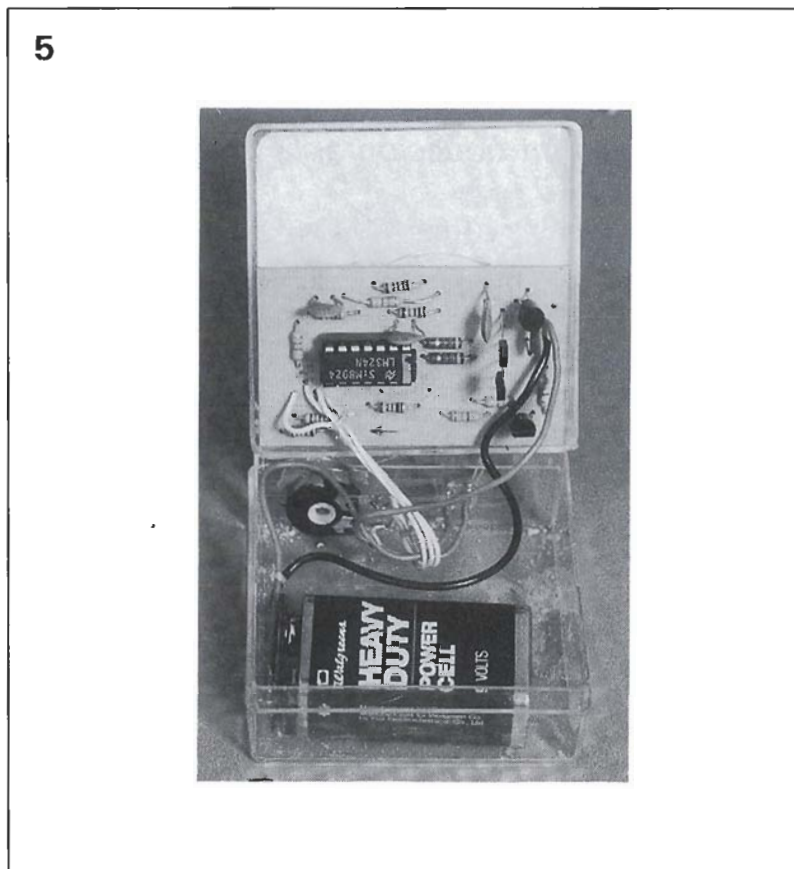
Es conveniente revisar todo el montaje en busca de cortos, soldaduras frías o cables sueltos antes de colocarlo en la caja.
